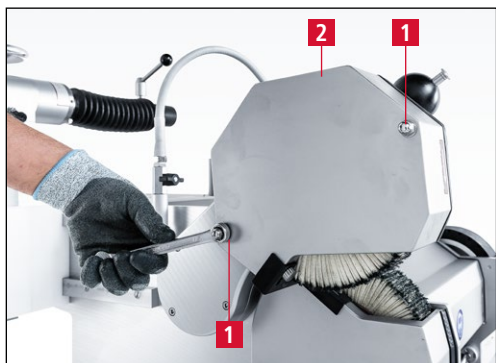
Ослабление колпачковых гаек верхнего полировального блока
